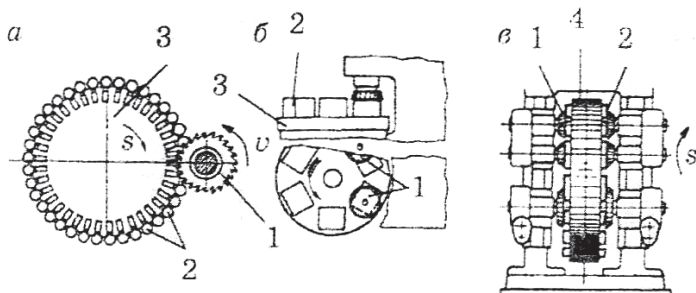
Примеры фрезерования деталей на фрезерных станках: а – карусельно-фрезерном с одним шпинделем; б – карусельно-фрезерном с двумя шпинделями; в – барабанно-фрезерном; 1 – фрезы; 2 – обрабатываемые детали; 3 – стол станка; 4 – барабан
